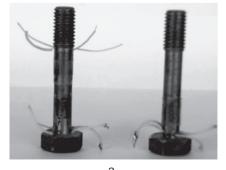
Испытываемые крепежные детали типовой конструкции с зазором (a) и предлагаемой конструкции (б)
